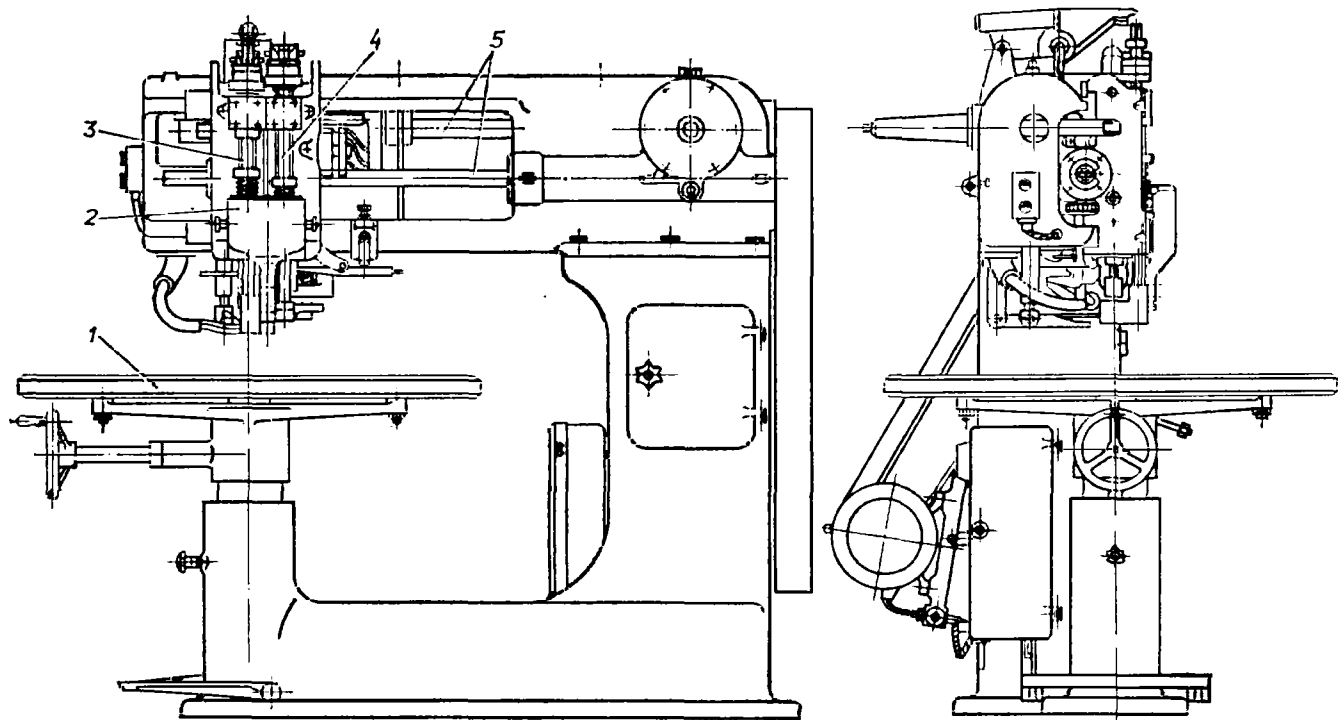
Схема сверлильно-присадочного станка СВСА:
